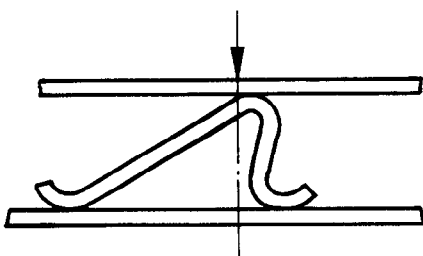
Cannelure commençant à se coucher, par exemple à la suite d'un mouvement latéral de l'éprouvette ou des plateaux
